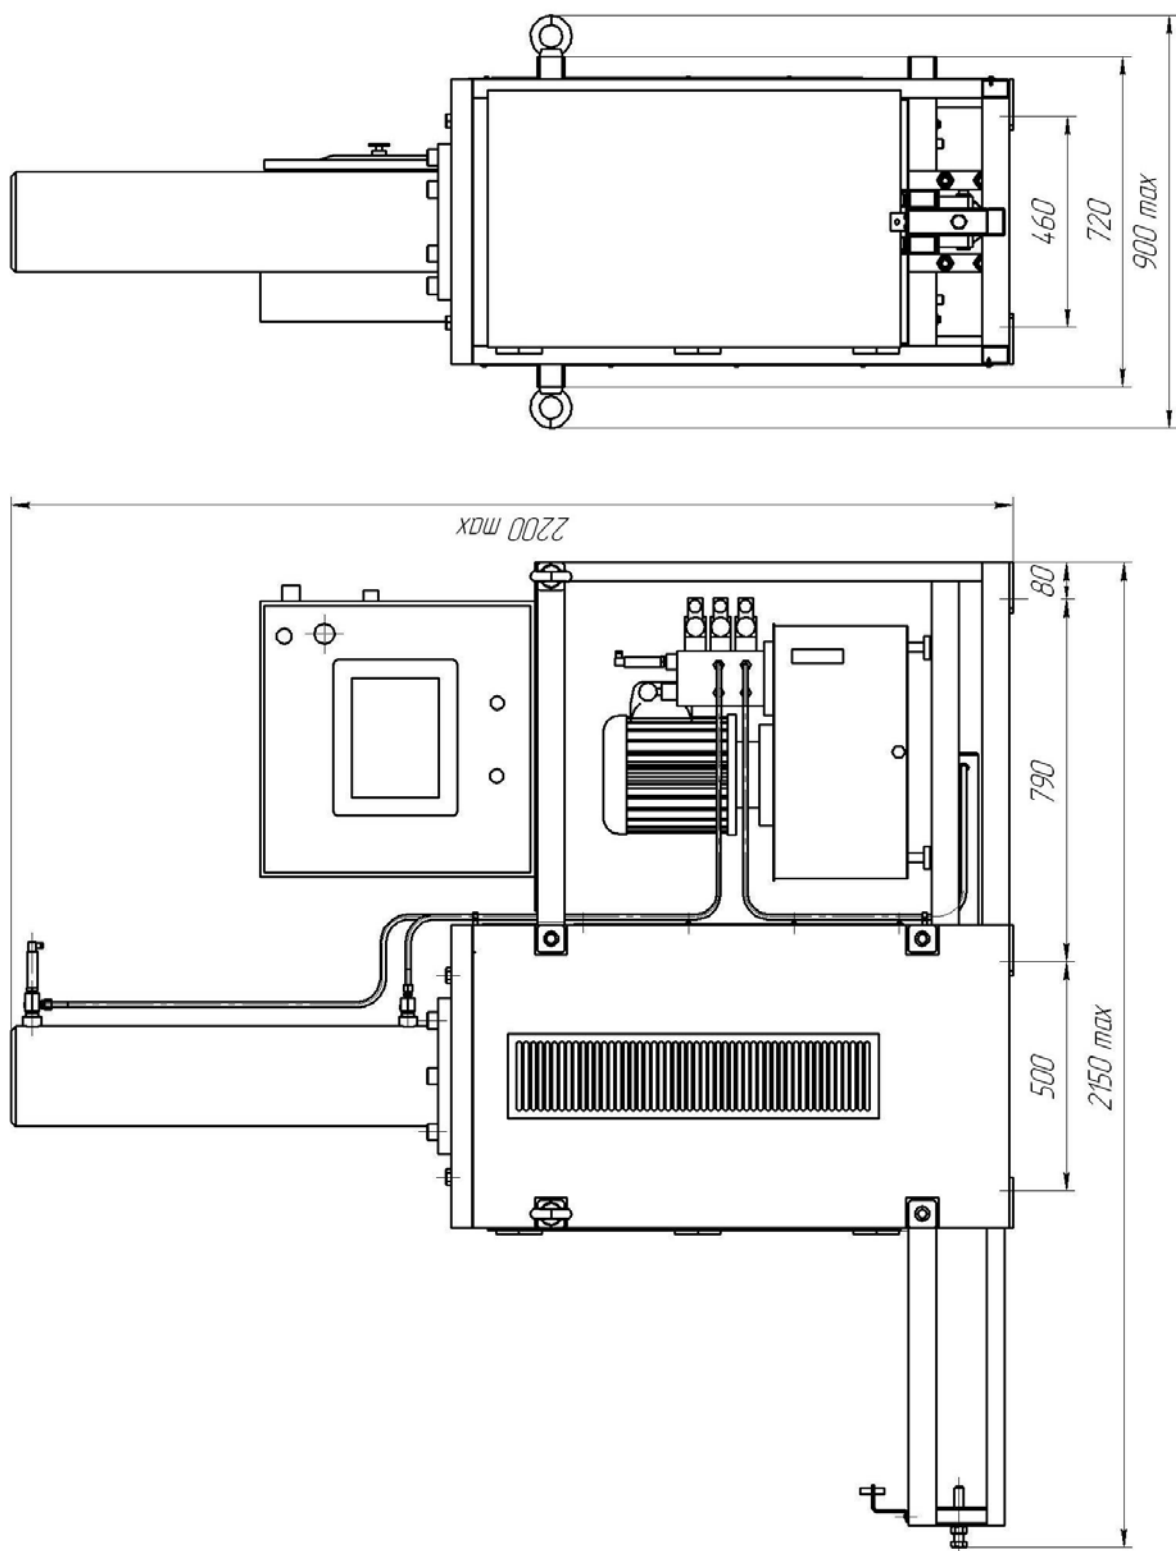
Габаритные и присоединительные размеры стенда СИП.ПЭТ
